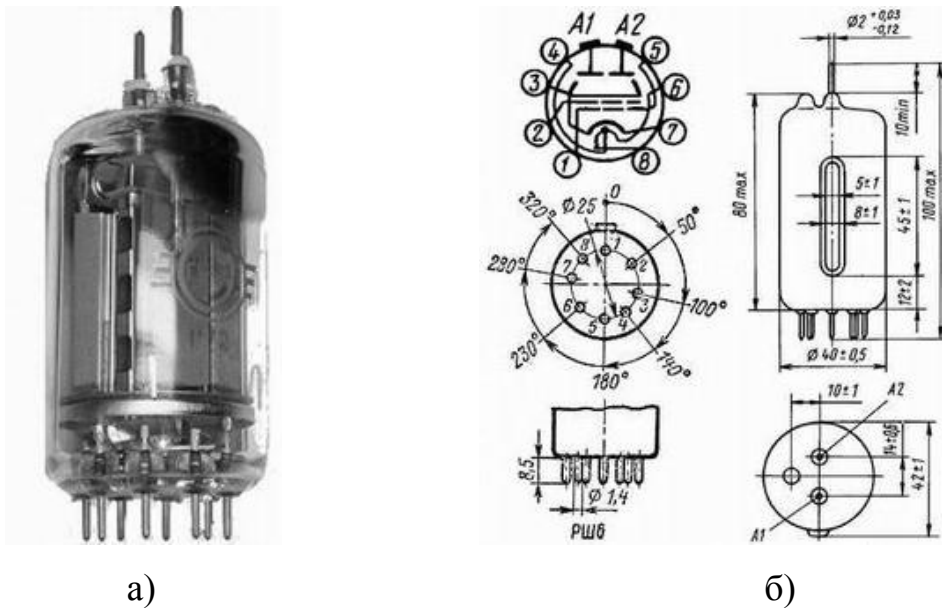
Лампа ГУ-19: а) загальний вигляд; б) габаритне креслення;
